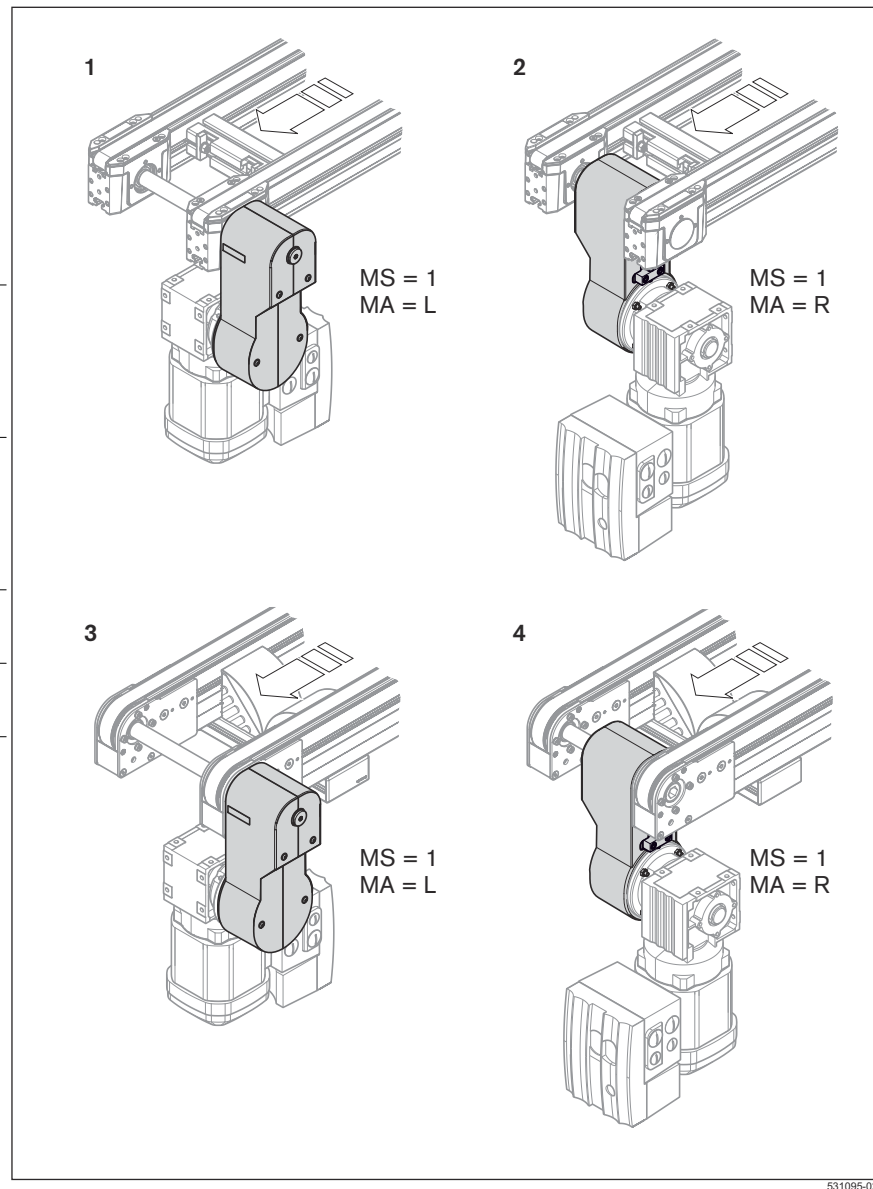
Positions de montage possibles sur la section à bande, exemples CSS/...
